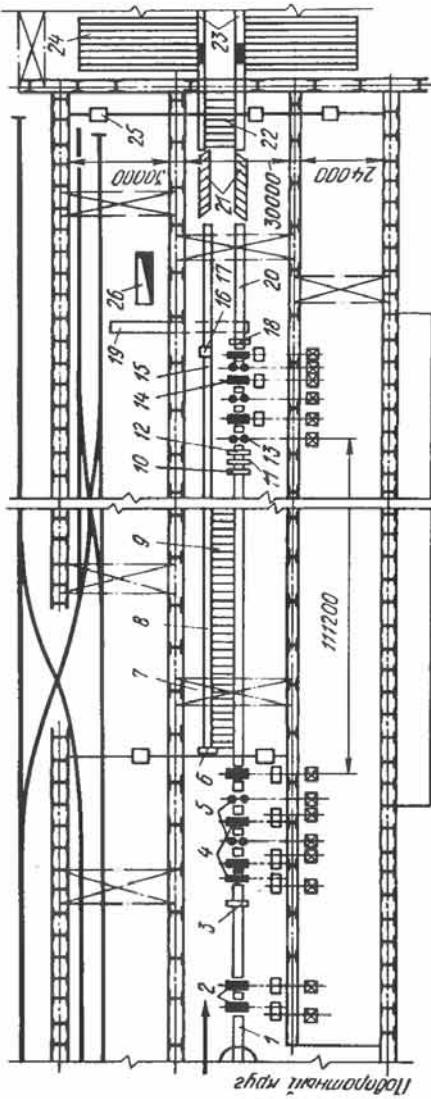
Схема расположения оборудования непрерывного заготовочного стана 900/700/500:
